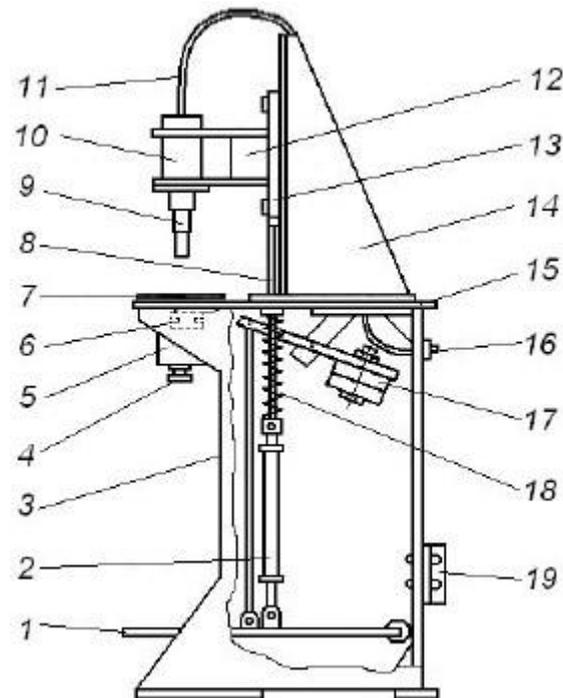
Конструктивная схема сварочной машины УПМ-21: 1 – педаль; 2, 8 – тяги; 3 – станина; 4 – регулирующий винт; 5 – механизм давления; 6 – концевой выключатель; 7 – пружинная опора; 9 – волновод-инструмент; 10 – сварочный узел (акустическая система); 11 – шланги для подвода охлаждающей воды; 12 – крон-штейн; 13 – суппорт; 14 – стойка; 15 – стол; 16 – штуцер; 17 – противовес; 18 – пружина; 19 – клеммная коробка
